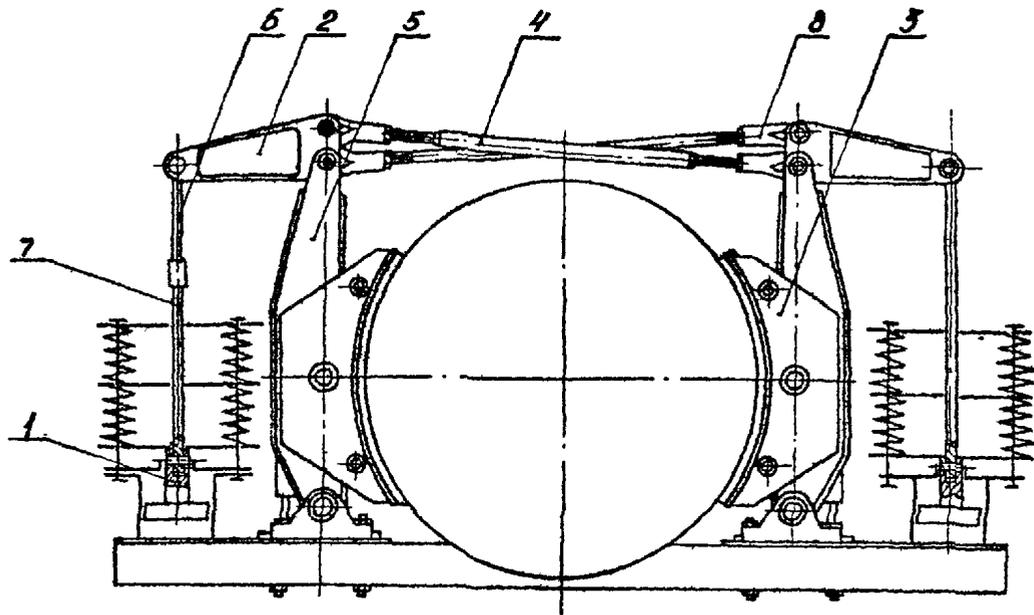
Тормоз с пружинным пневматическим безгрузовым приводом многоканатных подъемных машин Донецкого машзавода им.ЛКУ ЦШ5х4 и ЦШ5х8: 1 - шток; 2 - угловой рычаг; 3 - колодка; 4 - горизонтальная тяга; 5 - тормозная балка; 6,7 - тяга; 8 - головка шарнира.
